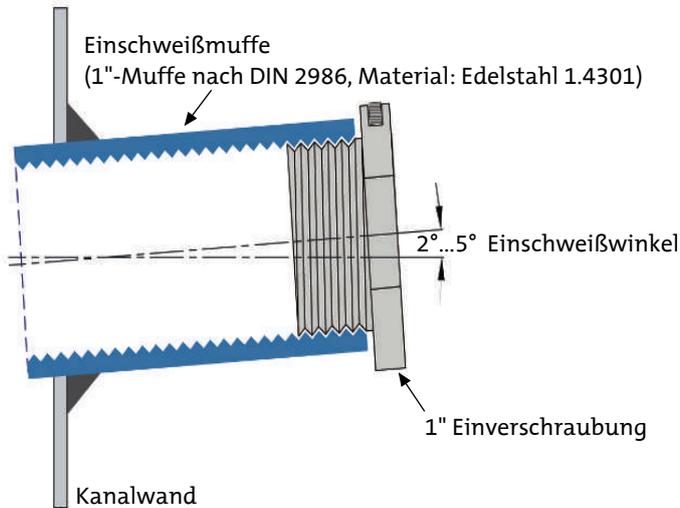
Einschweißmuffe (Gewinde)
